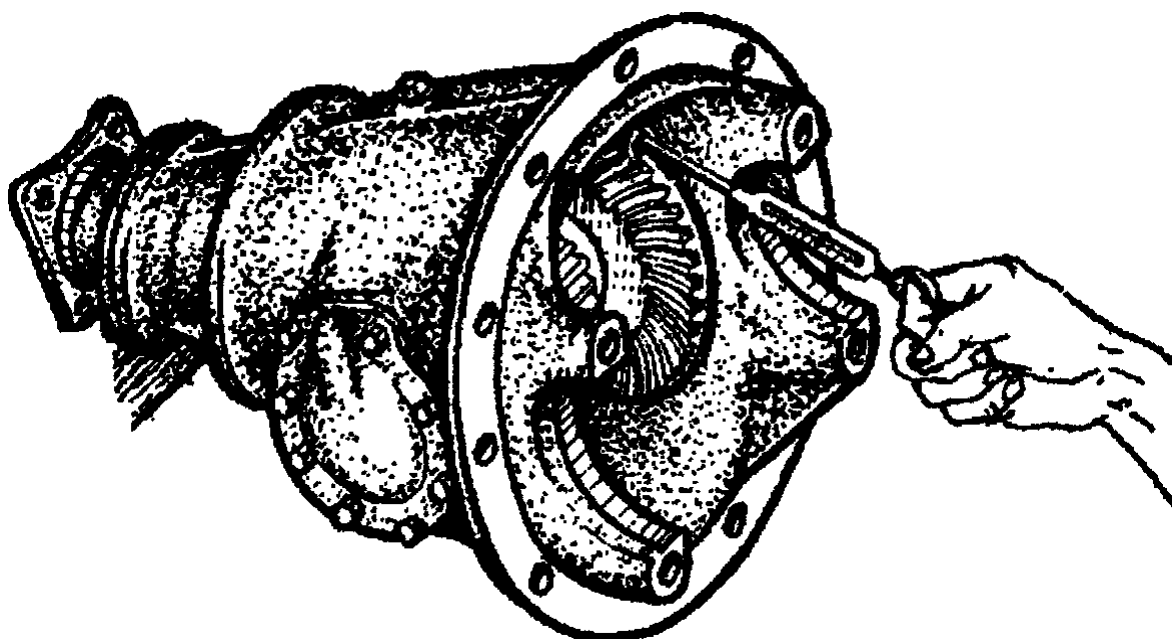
Перевірка зтяжки підшипників вала ведучої циліндричної шестірні редуктора заднього моста автомобіля ЗІЛ-130
